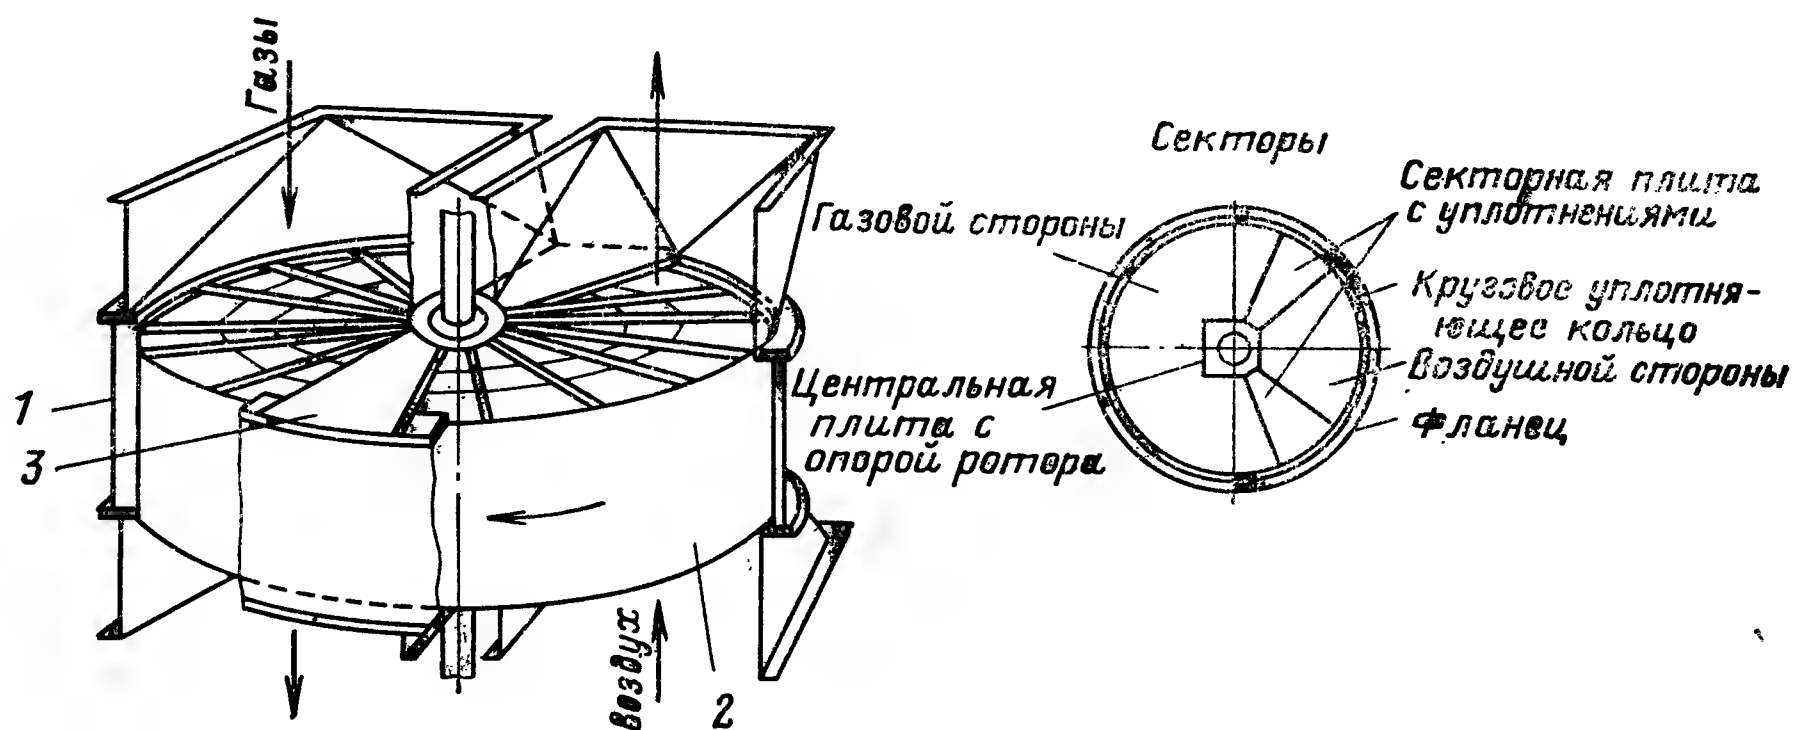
Регенеративный воздухоподогреватель с набивкой из стальных листов.
